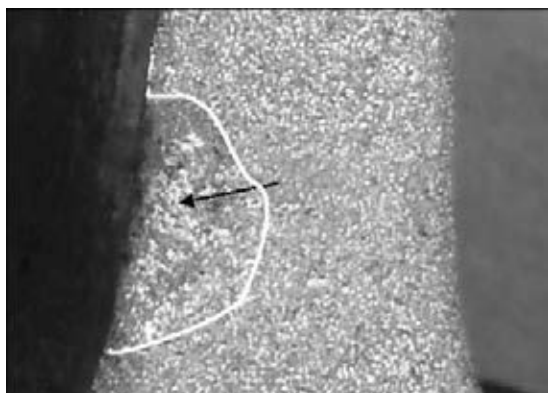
Железомарганцовистые силикаты на поверхности излома сварного соединения рельсов
